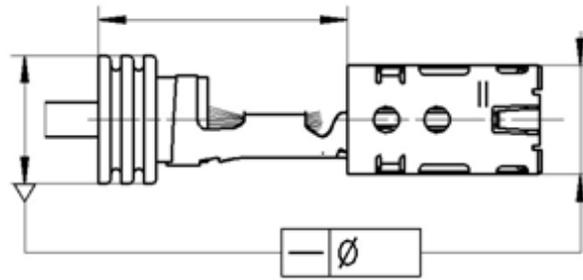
Position der ELA im Anschlagbild der Normteilzeichnung
